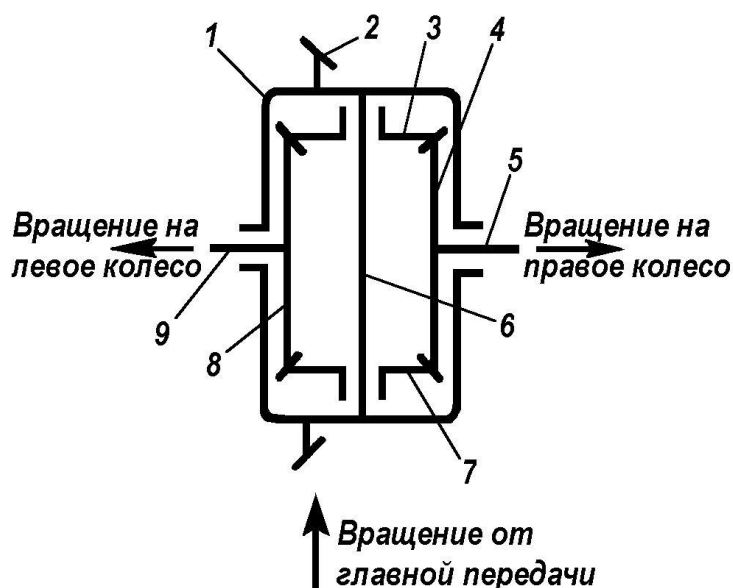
Схема простого дифференциала с коническими зубчатыми колесами:
